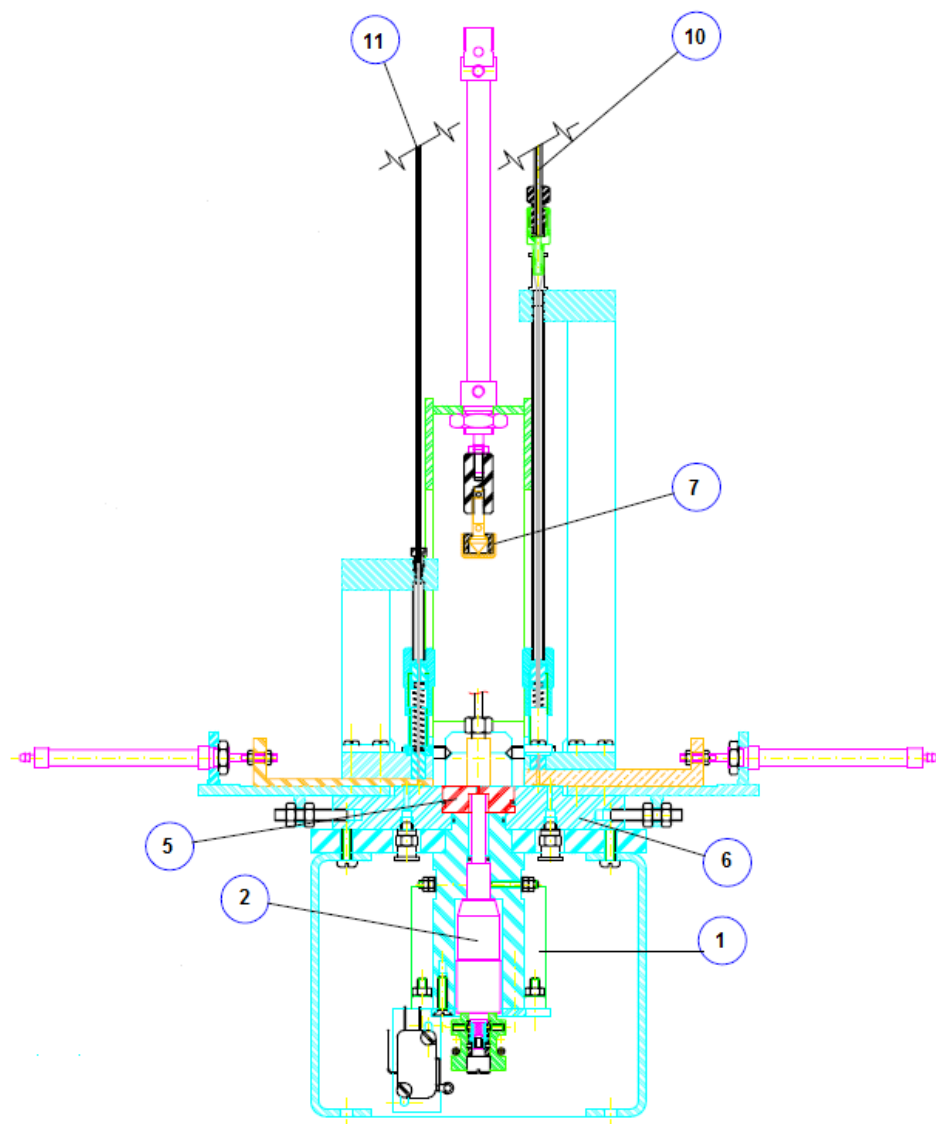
Corte frontal do dispositivo de soldagem constituído por: motor de passo (1), micrômetro (2), suporte de fixação (5), base de ajuste (6), sensor elétrico de posição (7), mangueira para alimentação de tubo de titânio (10) e mangueira para alimentação de fios de prata (11)
